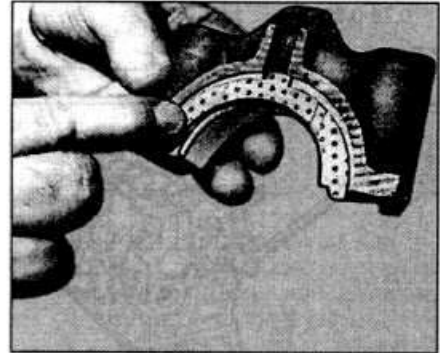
Установка крышки среднего коренного подшипника и упорных полуколец
